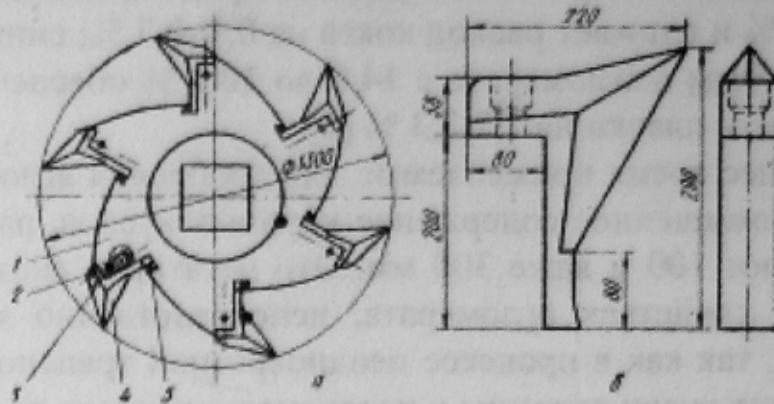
Звездочка одновалковой зубчатой дробилки: а – с самозатачивающимися зубьями; б – конструкция завода "Запорожсталь":
